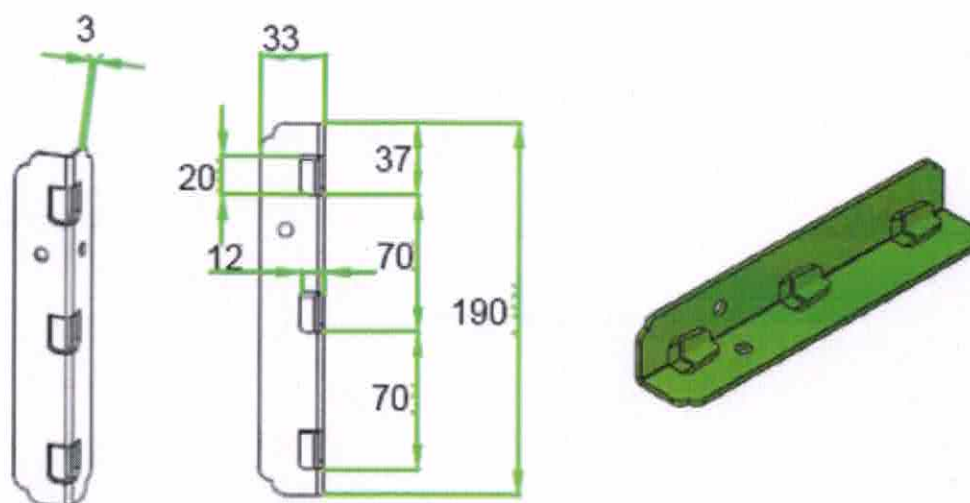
A – Dispositivo de encaixe fixado nas longarinas, opção de uso em substituição ao dispositivo da Figura 10 (medidas em milímetros)
